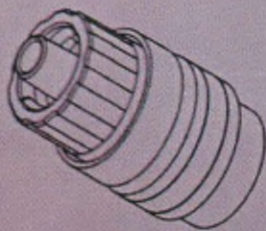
Уплотнительный колпачок. Вторичная упаковка.
